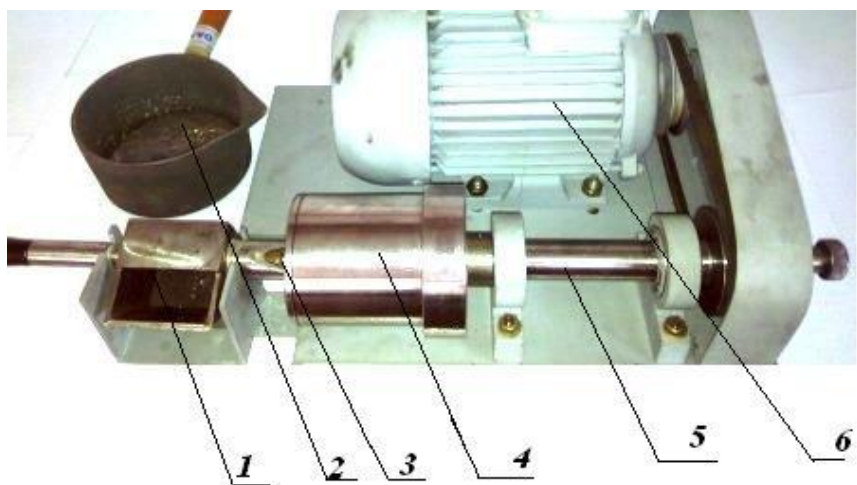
Лабораторная установка центробежного литья: 1- заливочная труба, 2-заливочный ковш, 3- мундштук, 4- изложница, 5- трансмиссионный вал, 6 – электродвигатель.
